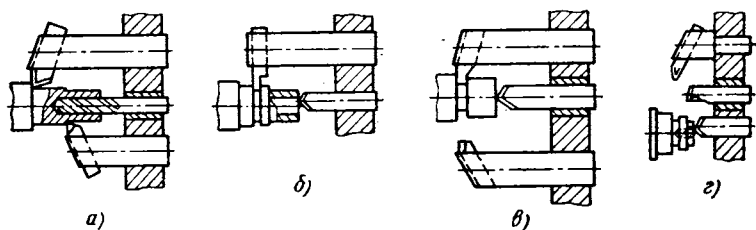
Приемы обработки деталей на станках с горизонтальным расположением оси револьверной головки
